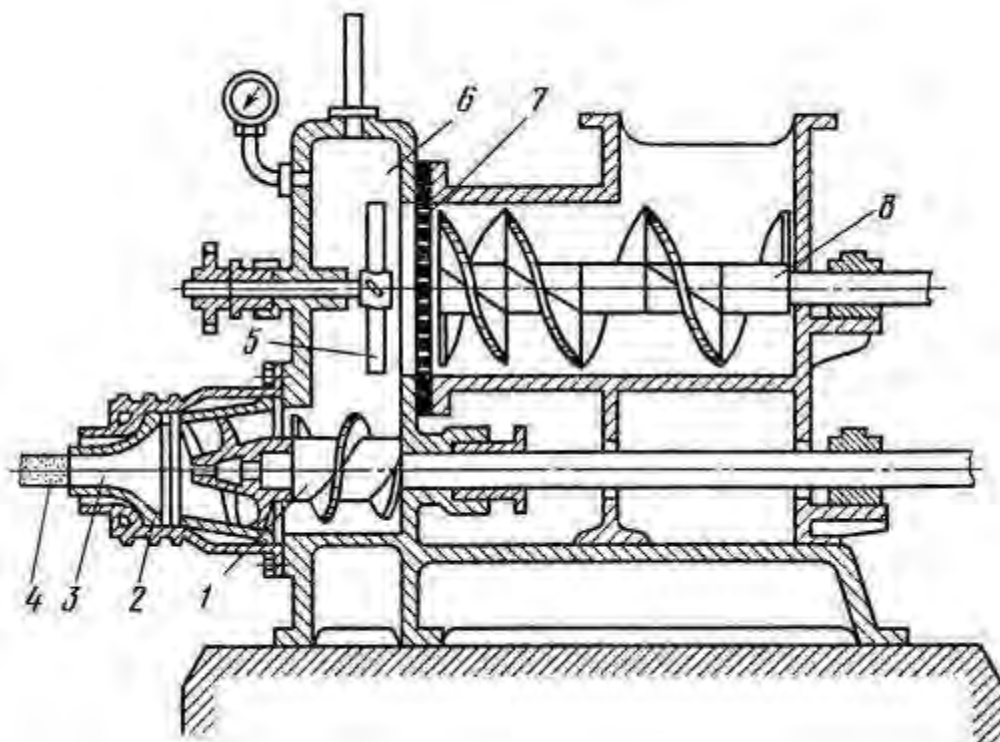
Ленточный вакуумный пресс: 1 - винтовой вал, 2 - конусная головка, 3 - матрица-мундштук, 4 - глиняный брус, 5 - нож, 6 - вакуумная камера, 7 - решетка, 8 - винтовой конвейер
